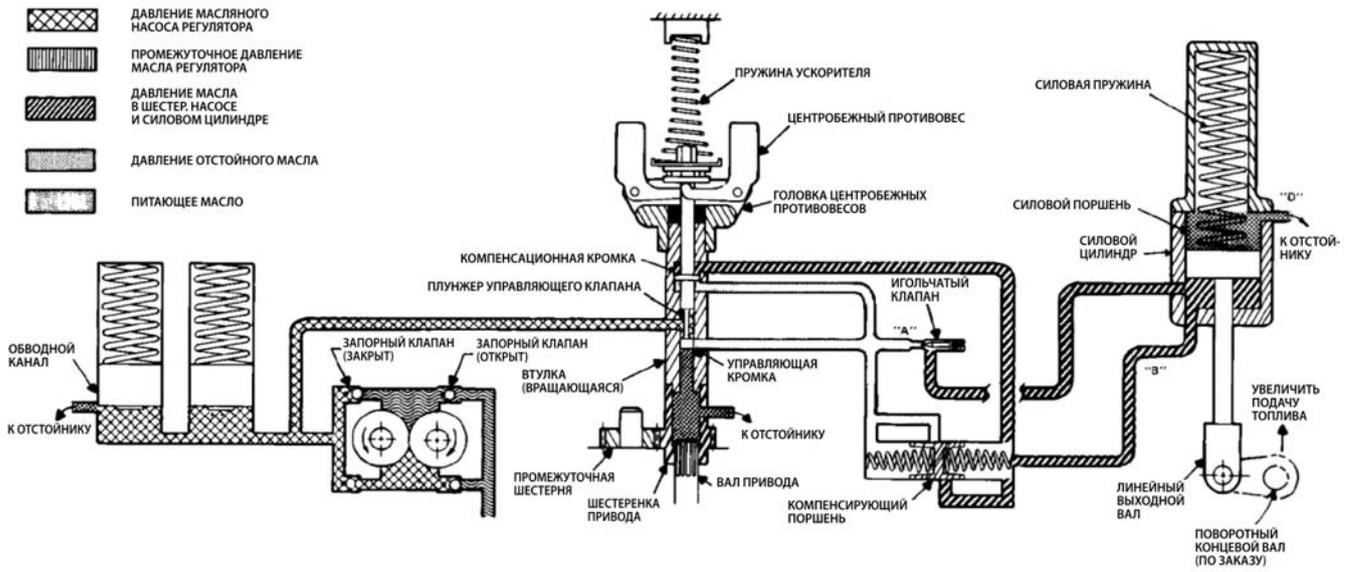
Схема подпружиненного силового цилиндра (16 Дж)
